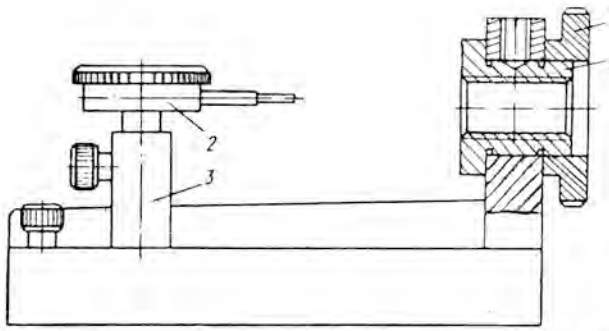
,9 Приспособление для контроля "качки" в окулярной резьбе
